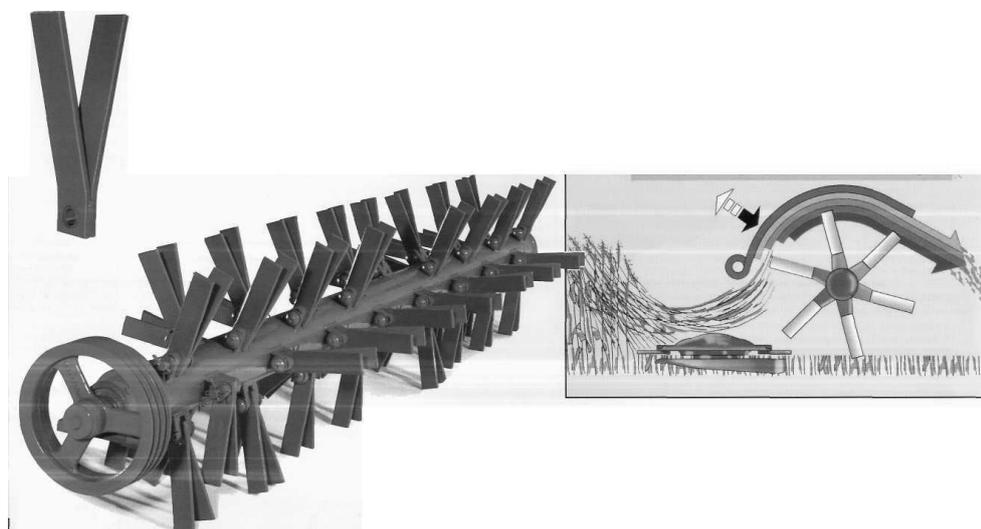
Устройство и схема работы плющильно-вспушивающего аппарата с V-образными стальными битерами
